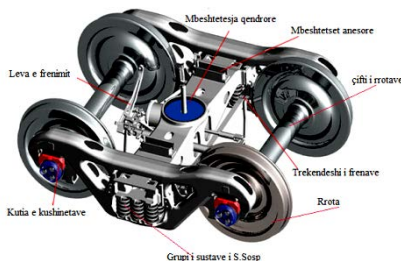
Pamje e konstruksionit të një karrete të tipit 18-100
